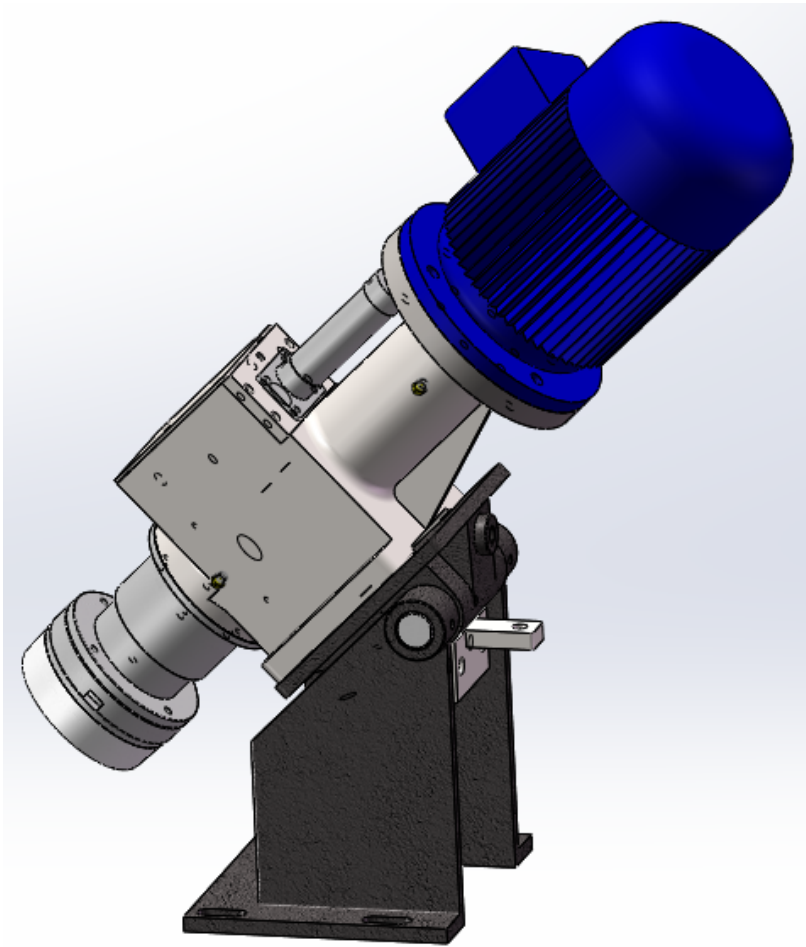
上倒角磨头 Figure 2-2 Upper chamfer head
